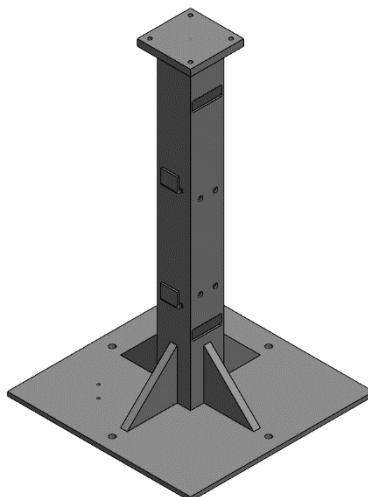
Segunda fase da construção do suporte do robô colaborativo.
